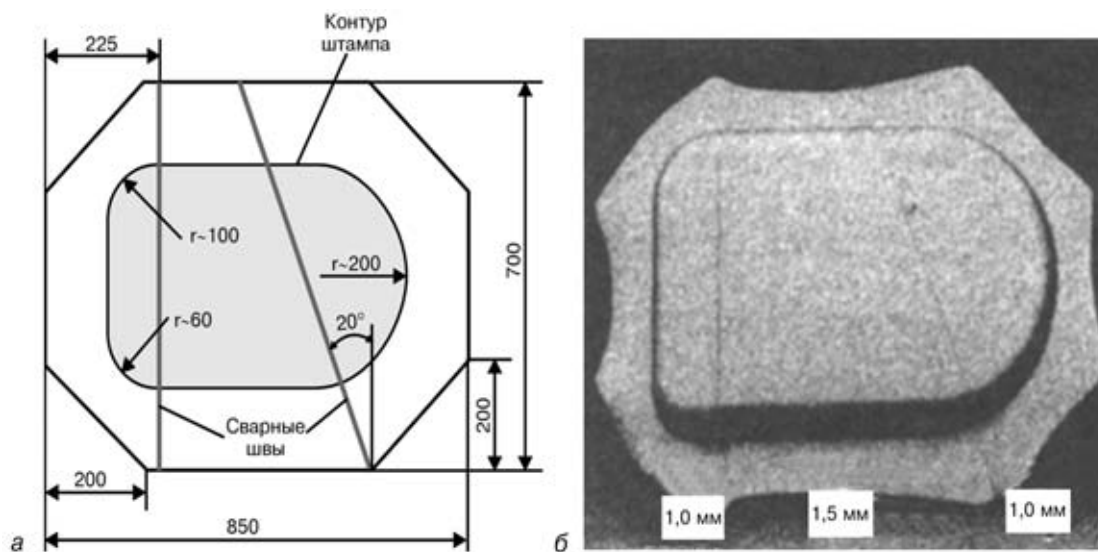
Оптимизированная по условиям штамповки размерная ССЗ, сваренная из трех элементов: а — схема тонколистовой заготовки; б — отштампованная деталь
